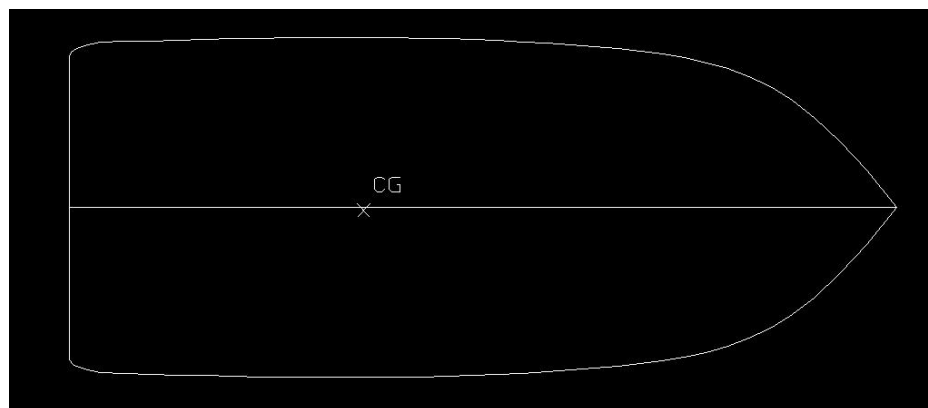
Vista del centro de gravedad en planta en la condición de mínima carga. FUENTE PROPIA.
